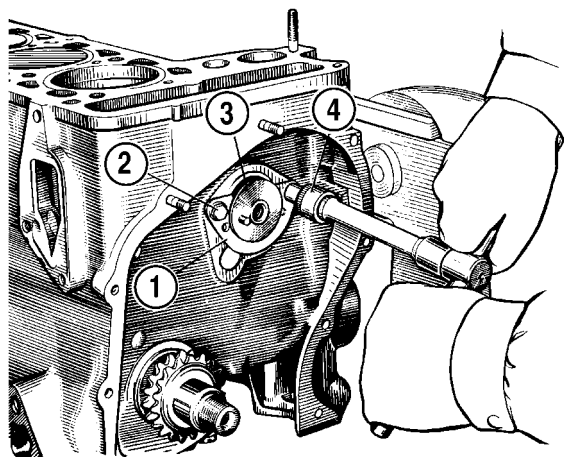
Снятие упорного фланца распределительного вала:
